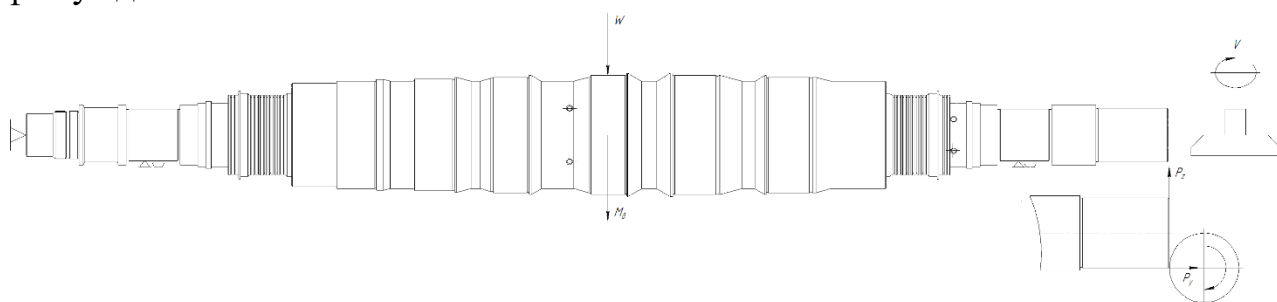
Сили, що діють на заготовку при обробці деталі
